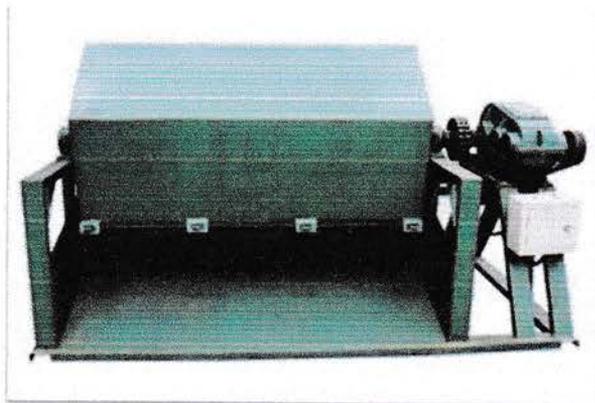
Mesin Pembuat Paku (*Nail Making Machine*)
